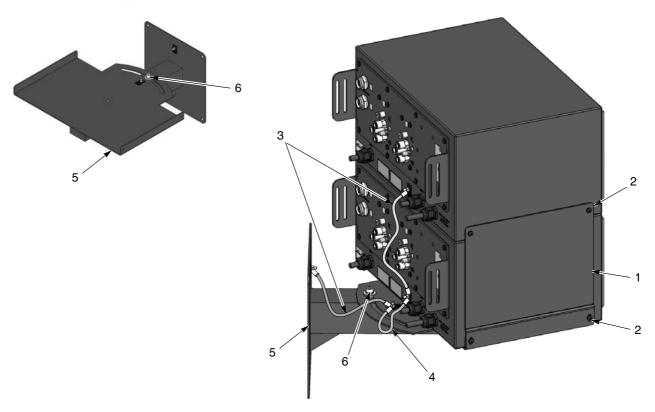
Montaggio del controller per due pistole con staffa di montaggio a parete opzionale
